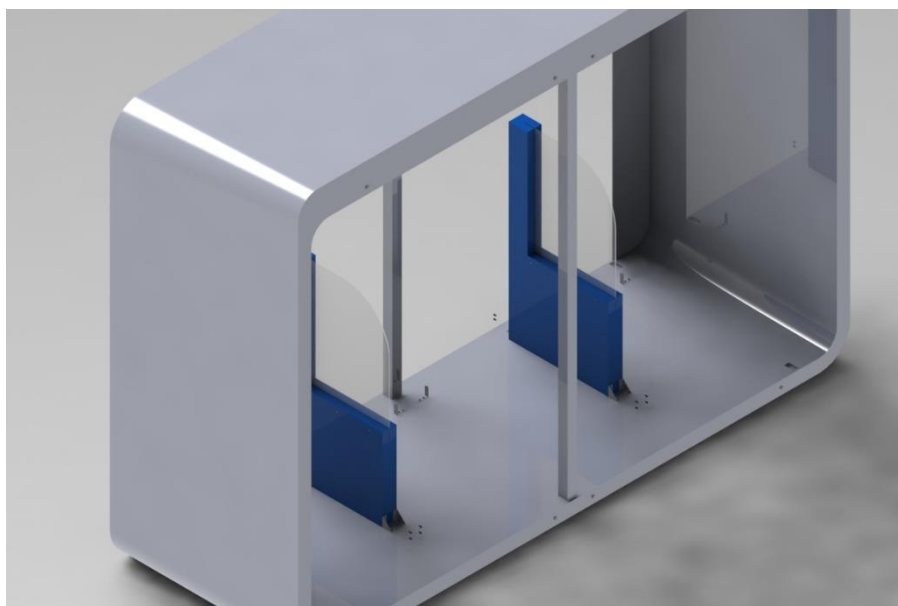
Ensamblaje conjunto. Unión roscada de escuadras y soporte placa.
